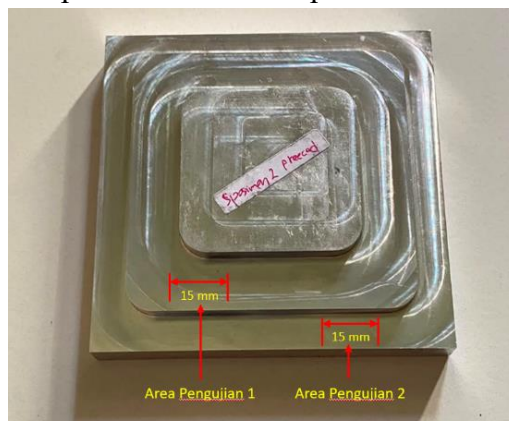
Produk hasil *machining* FreeCAD spesimen 1
